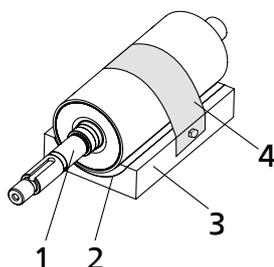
Вспомогательное приспособление для монтажа/демонтажа гильзы подшипника со стороны привода
